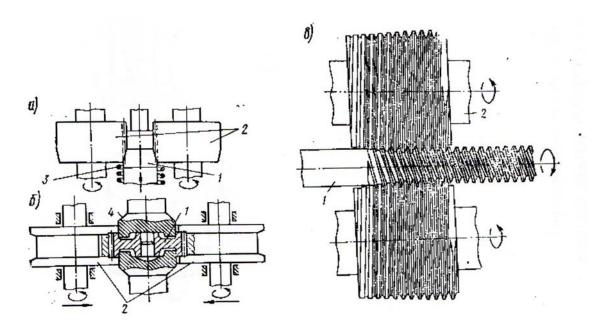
Схемы накатки: а – зубьев шестерен с осевой подачей заготовок; б – зубьев шестерен с радиальной подачей зубчатых валков; в – резьбы методом косой прокатки
